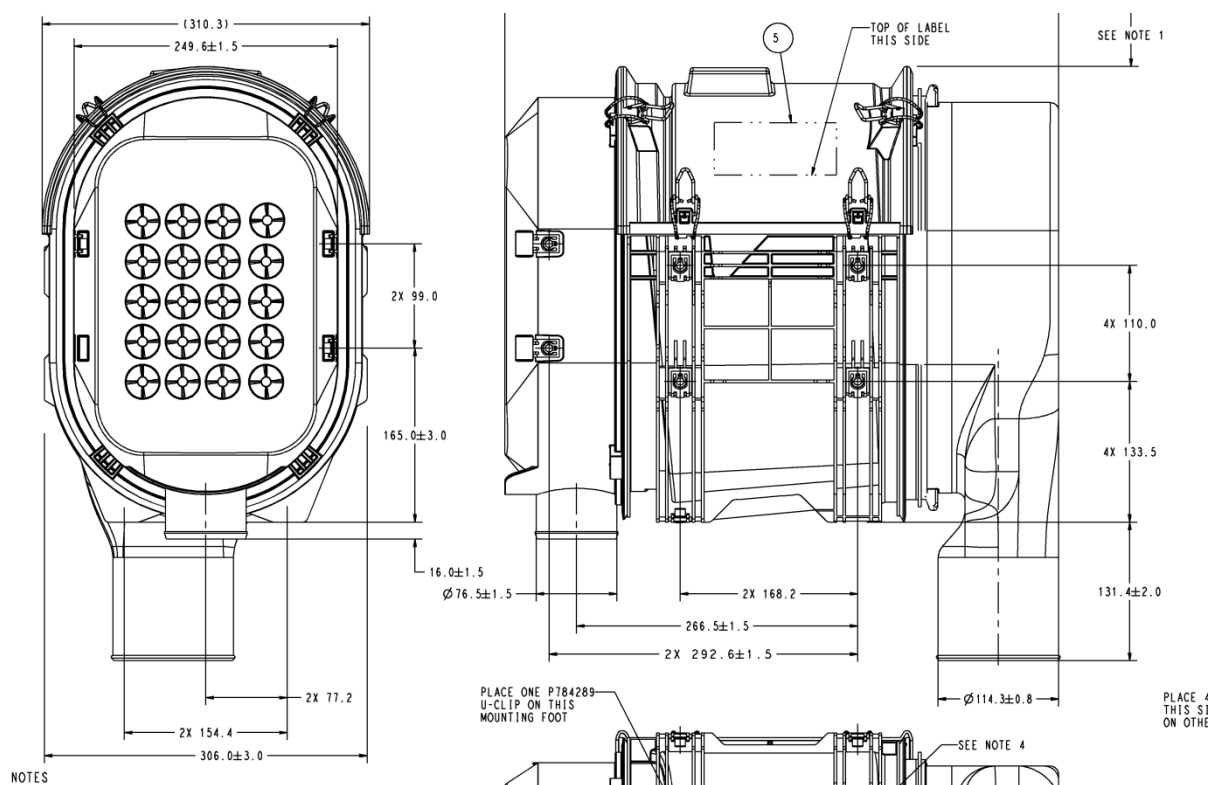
Parte de um desenho técnico do pré-filtro com 20 spins
